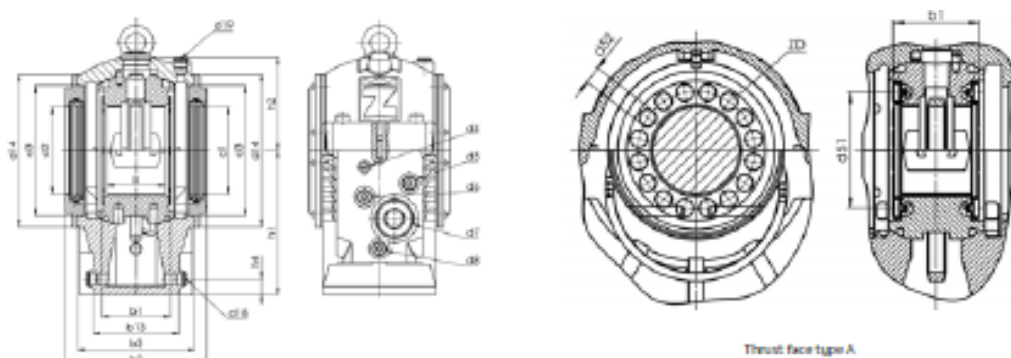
Zobrazení skutečného uspořádání ložisek [5]
